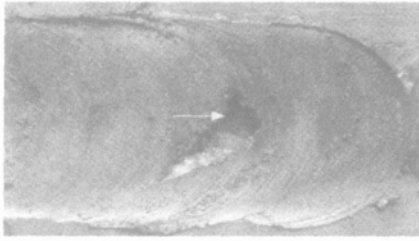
转速 1300r/min, 焊速 110mm/min 时焊缝上表面出现的孔洞缺陷
